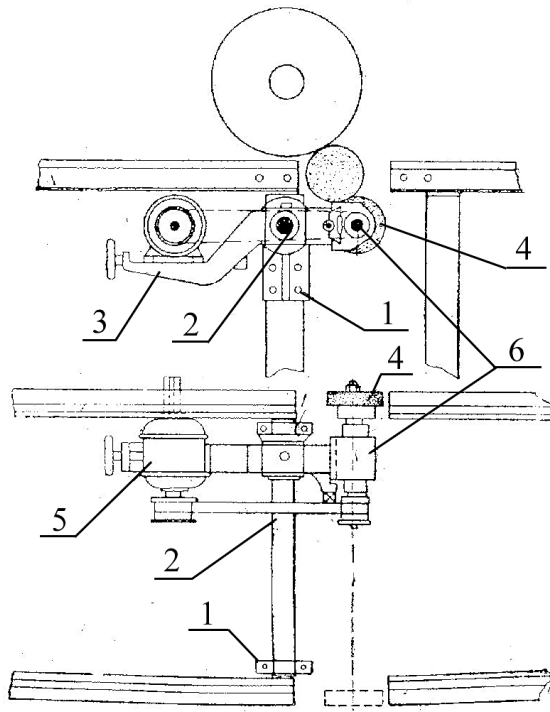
Схема приспособления для шлифования бандажей колесных пар без выкатки [2]
